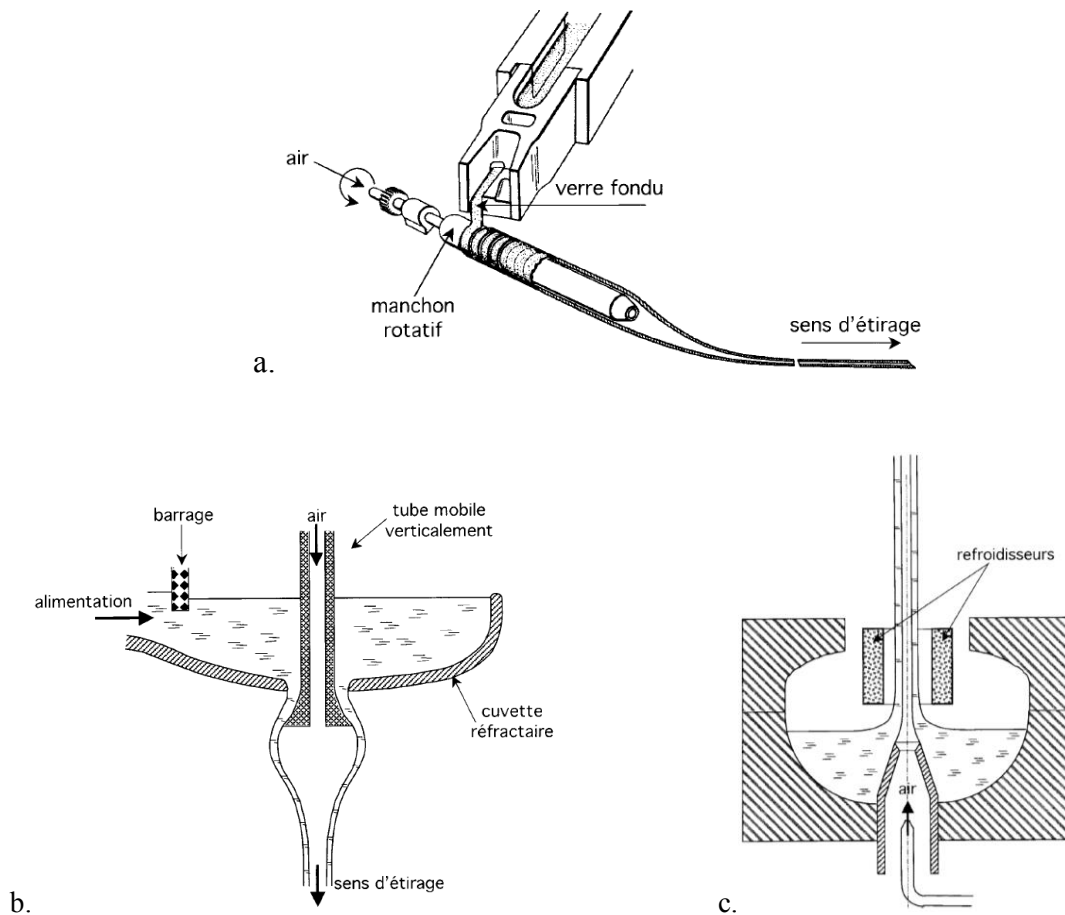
Représentation schématique des procédés Danner (a) et Vello par étirage vers le bas (b) et par étirage vers le haut (c) pour la fabrication de tube de verre [1].
